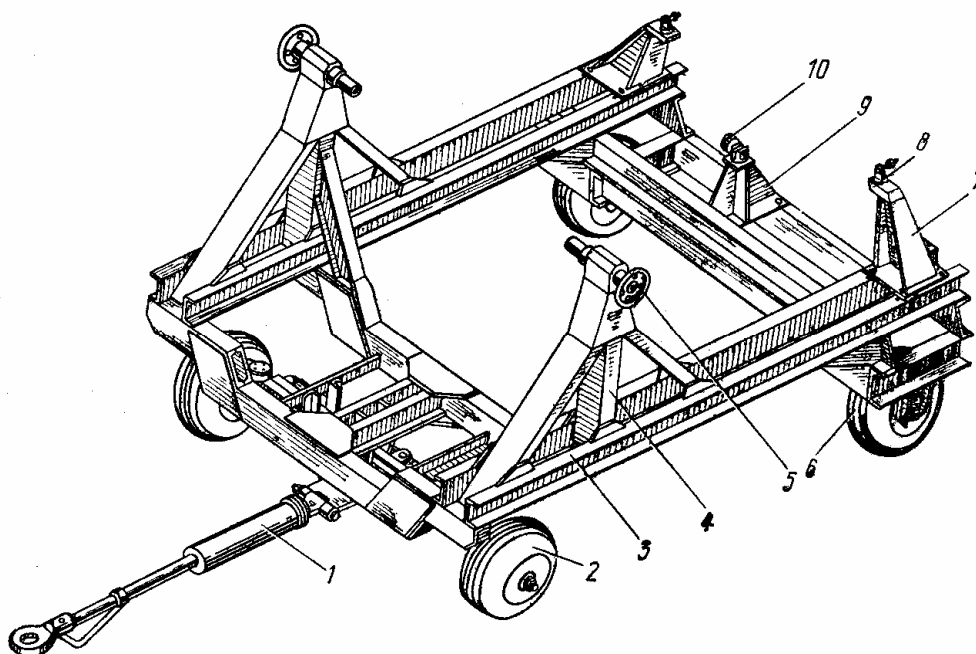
Тележка 7Я-3815-000-00 для транспортировки двигателя:
